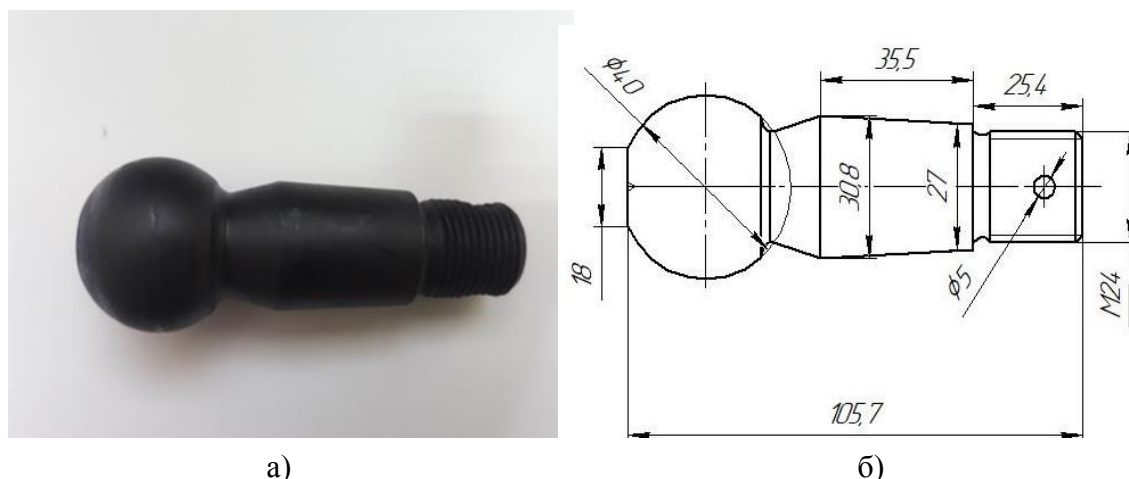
Шаровой палец: а - общий вид; б - рабочий эскиз
